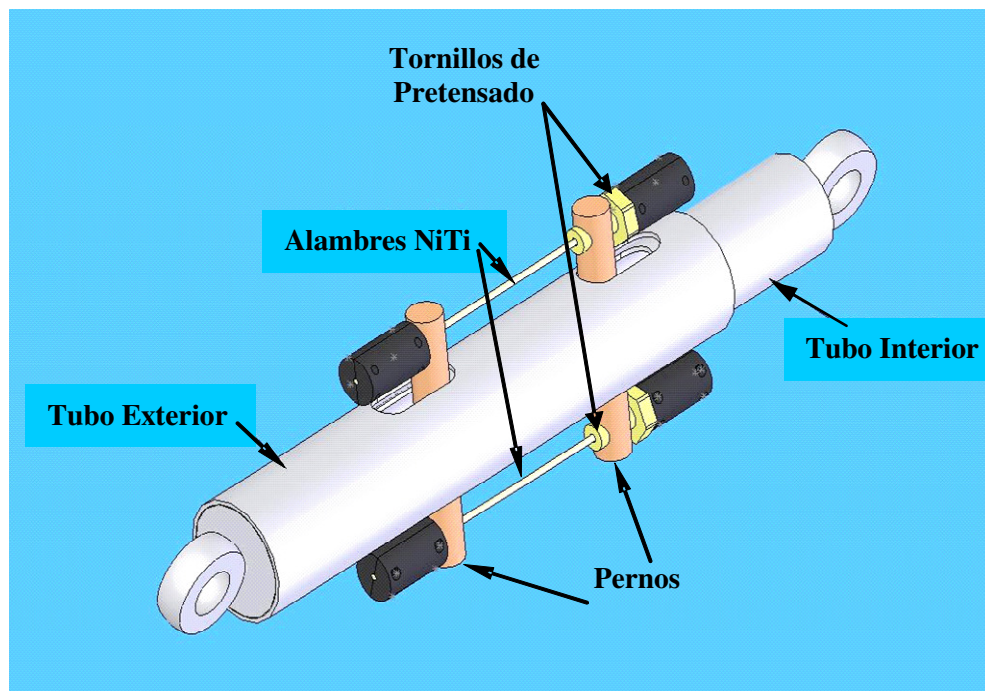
Vista en Perspectiva del conjunto armado del dispositivo diseñado, construido y caracterizado en la máquina MTS 810.
